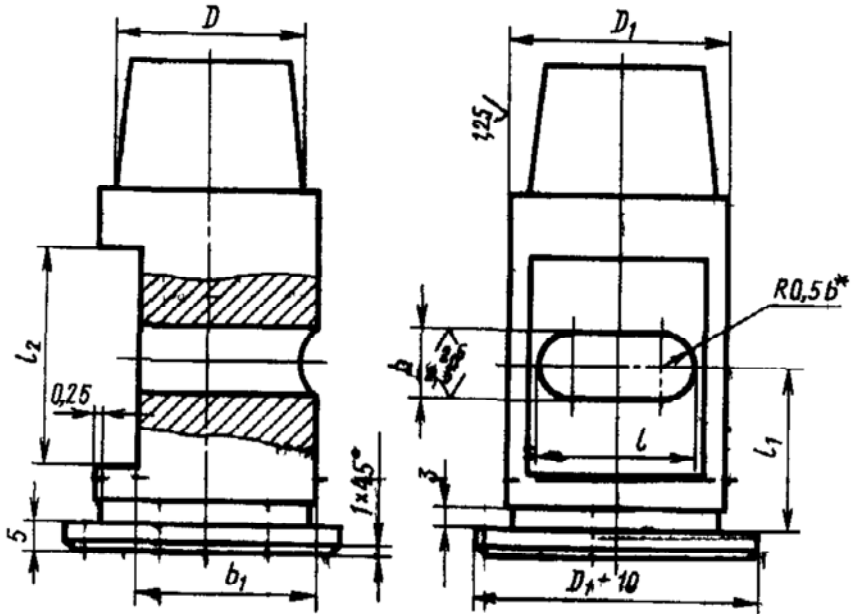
Конструкция стержней, удаляемых эксцентриковыми приспособлениями
